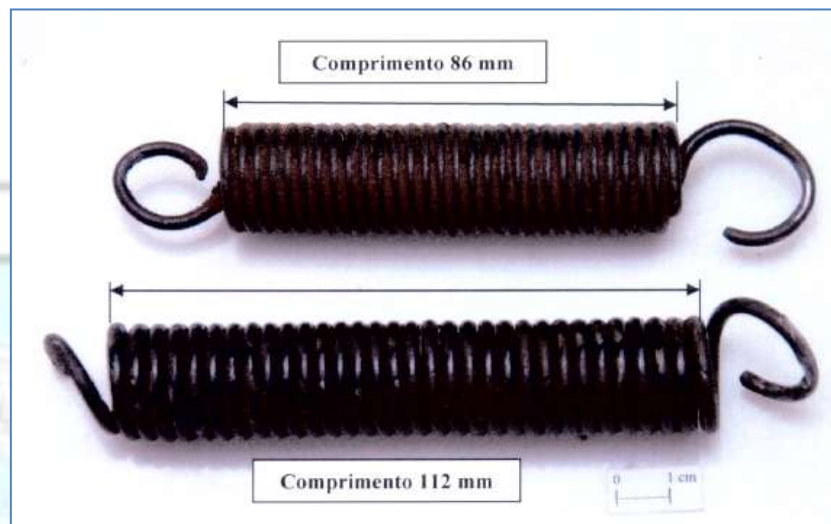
Molas externas do conjunto do trem auxiliar, com destaque para as dimensões diferentes.
